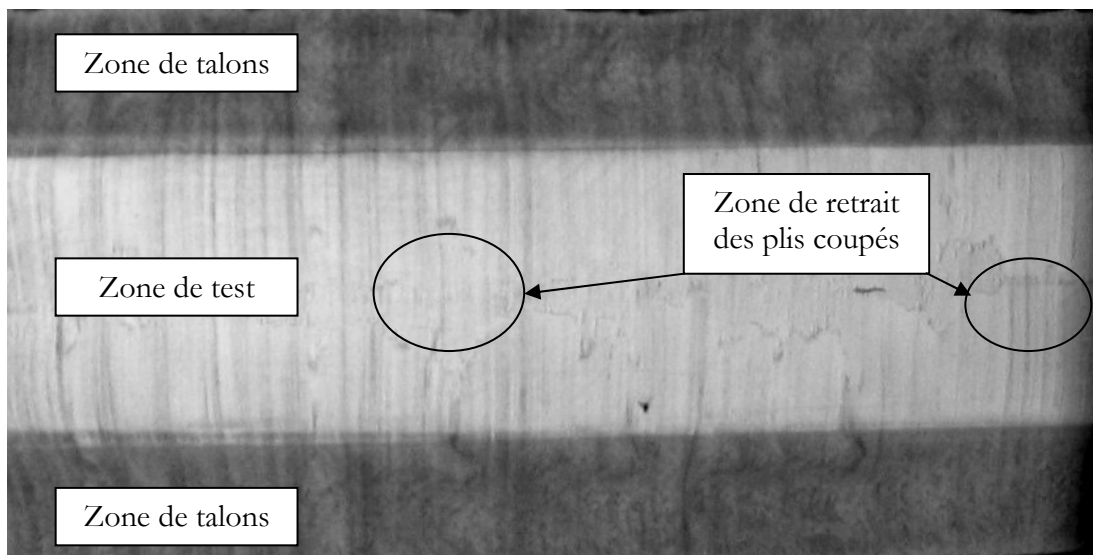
Plaque d'éprouvettes UD 0° après fabrication
